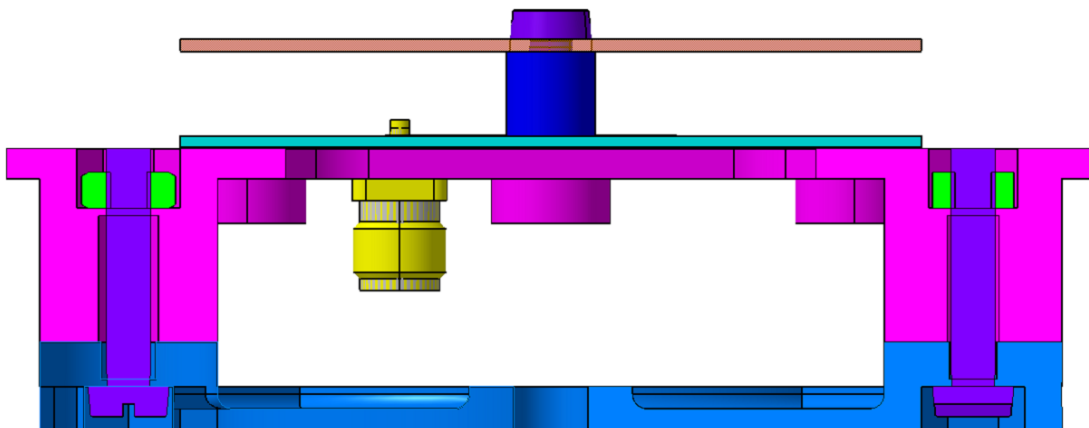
Vista lateral seccionada del parche y su estructura
